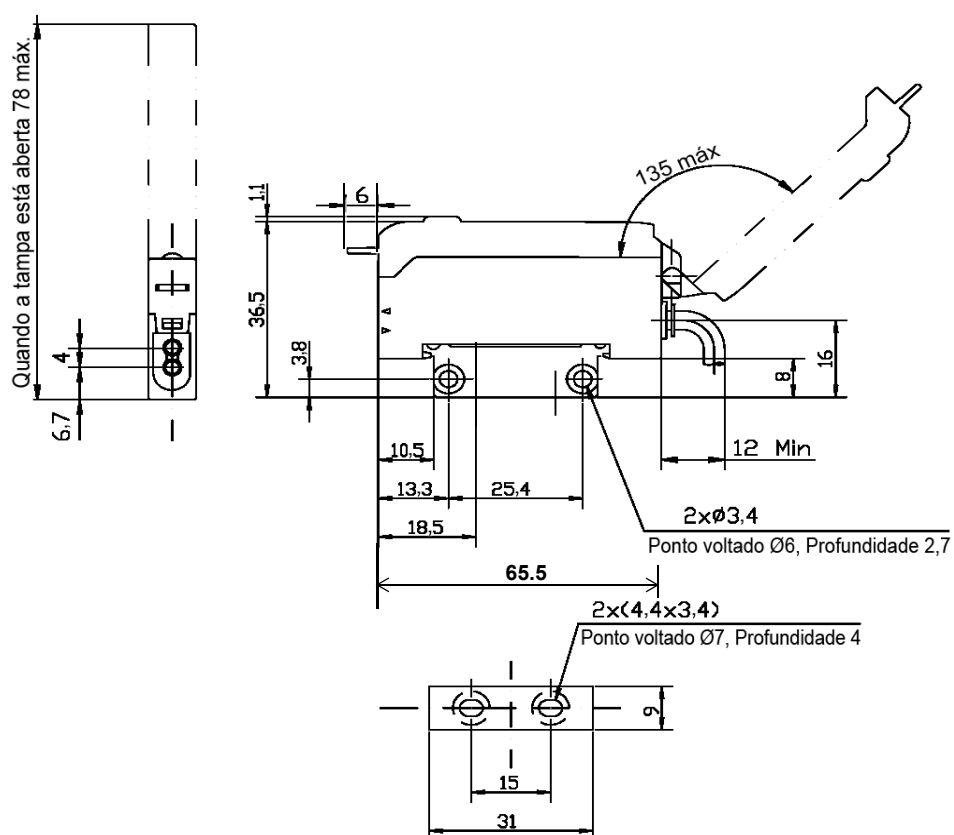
Célula fotoelétrica com dimensões de montagem de instalação
